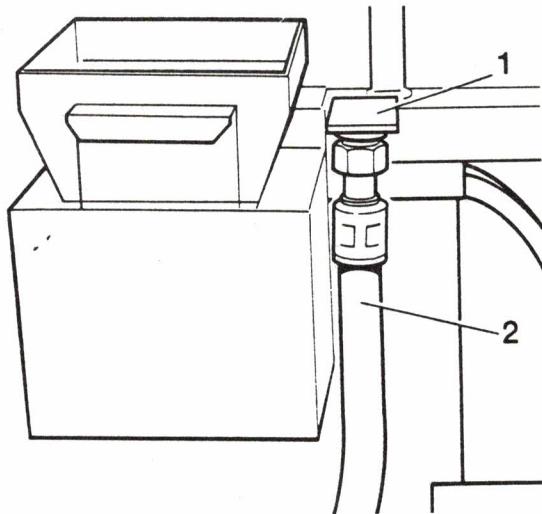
Ölablaßschlauch, Drucklufterzeuger (VerbrMot)
